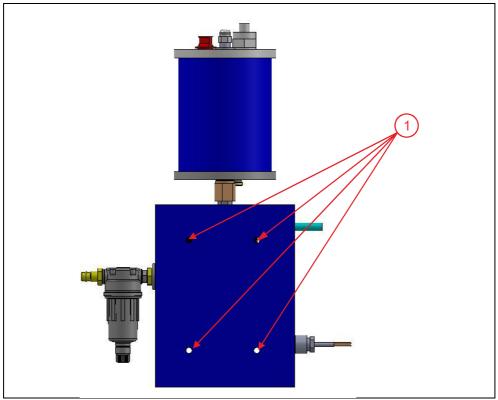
Minimalmengenschmiergerät mit Schrauben befestigen
